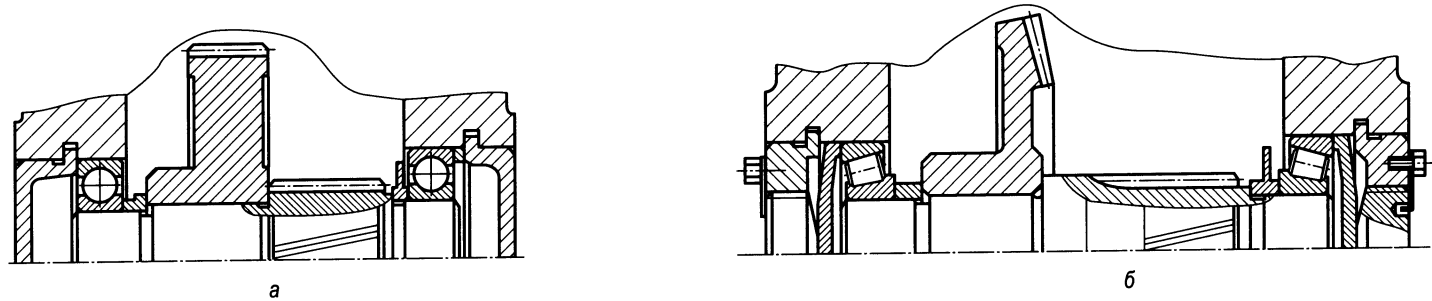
Промежуточный вал цилиндрического (а) и коническо-цилиндрического (б) редуктора
